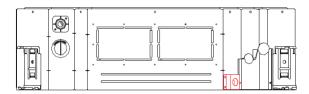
Support de serre-câble fixé sur le corps de la cassette
